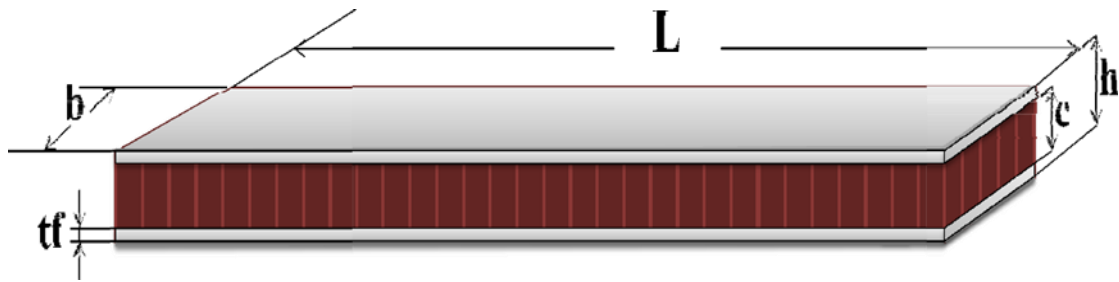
dimension d'une éprouvette sandwich selon la norme NF T 54-606
